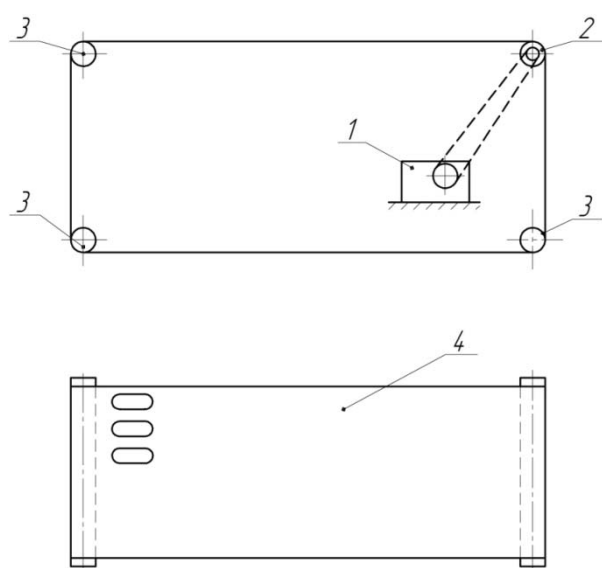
Схема картофелесортировки транспортерного типа: 1 – привод; 2 – ведущий барабан; 3 – поддерживающий барабан; 4 – транспортерная лента
